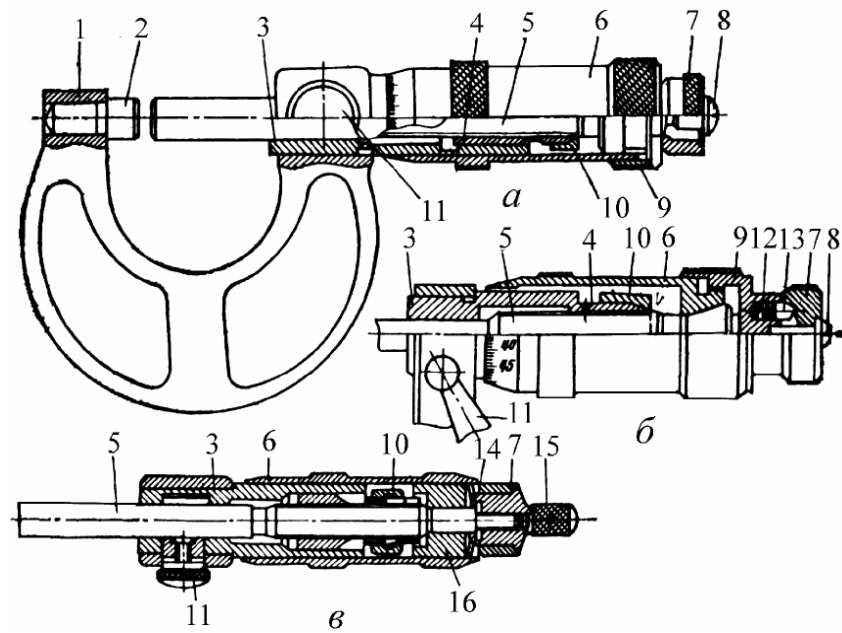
Тип МК, мікрометр гладкий: 1 – подковоподібна скоба; 2 – вимірювальна п'ята; 3 – стебло; 4 – мікрометрична гайка; 5 – мікрометричний гвинт; 6 – барабан; 7 – храповик; 8 – кріпильний гвинт; 9 – тріскачка; 10 – регулювальна гайка; 11 – стопорний пристрій; 12 – тарувальна пружина; 13 – штифт із скосом; 14 – пружинне кільце; 15 – гайка; 16 – циліндрична втулка
